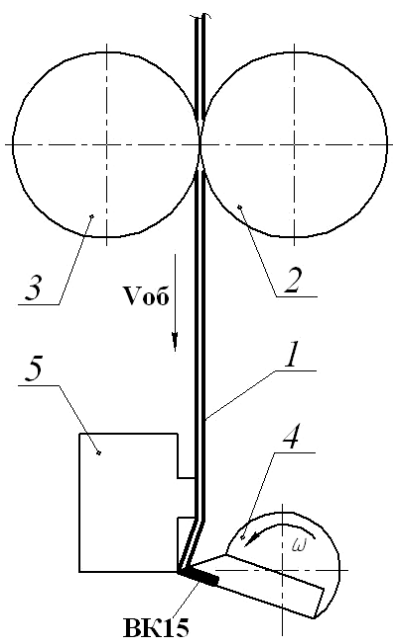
Схема поперечного перерізу паперорізального вузла ірисозагорткового автомата ІЗМ: 1 – обгортка; 2,3 – ролики; 4 – вал з обертовим ножом; 5 – нерухомий ніж
